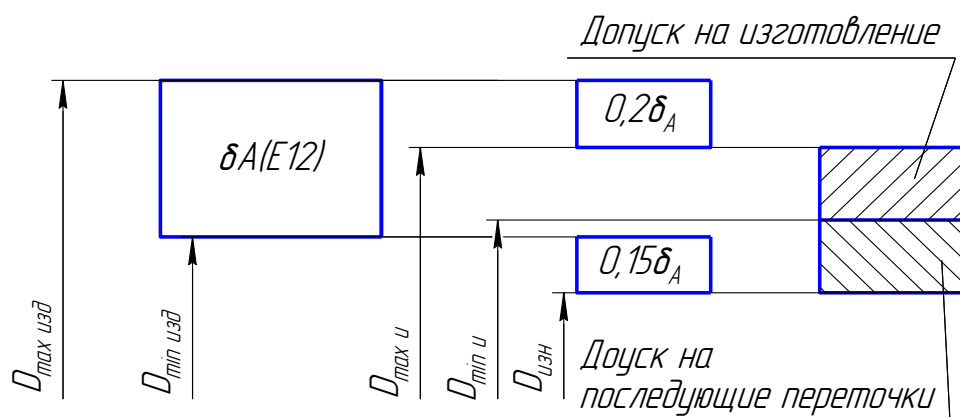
Схема расчета исполнительного размера калибрующей части развертки
